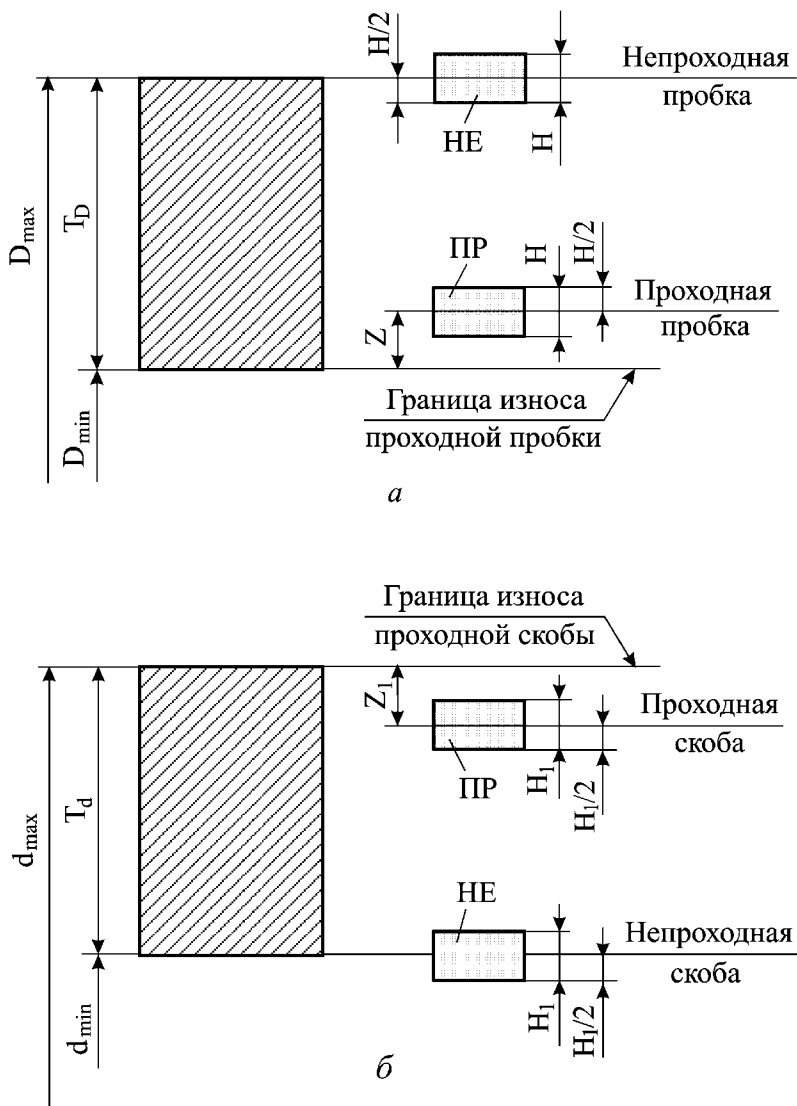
Схемы расположения полей допусков гладких калибров для контроля отверстий (а) и валов (б) с номинальными размерами до 180 мм и допуском изготовления по IT9-IT17
